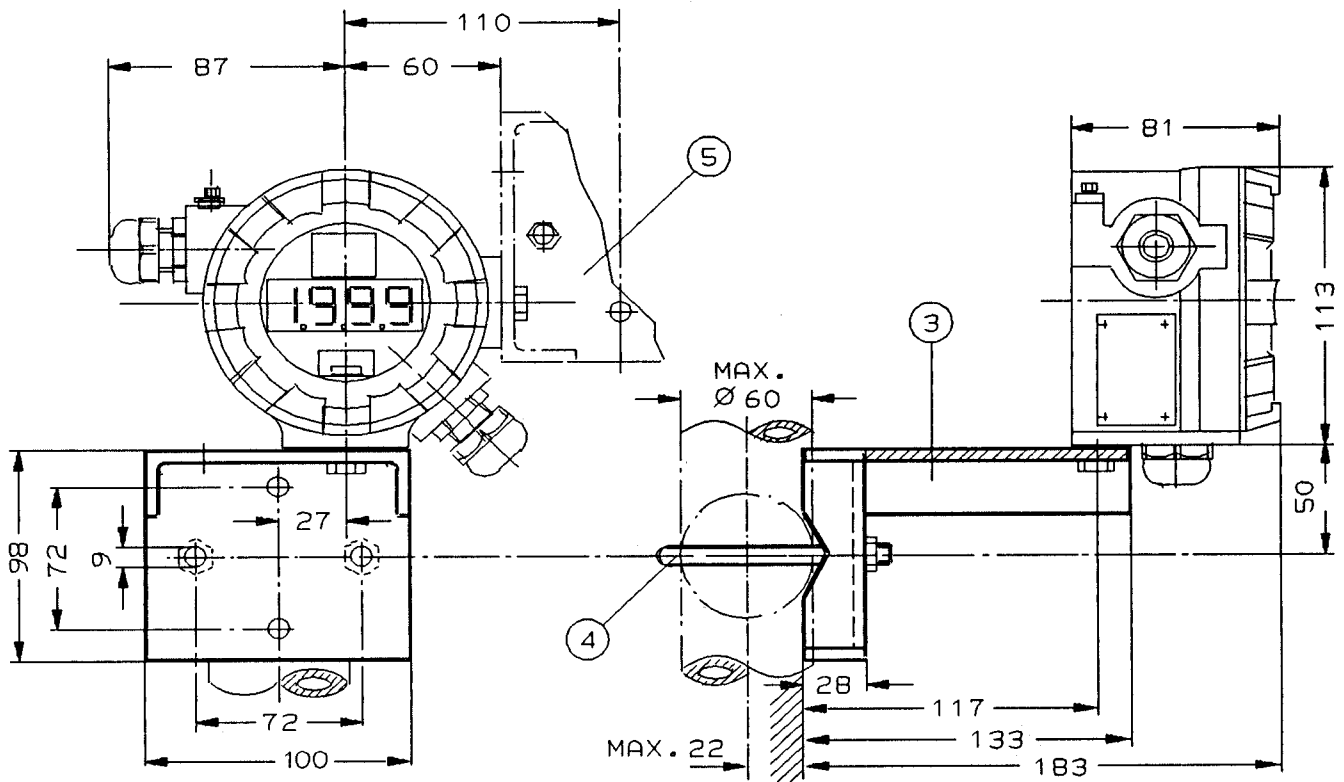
Abmessungen mit Montagewinkel für Rohr- und Wandmontage
